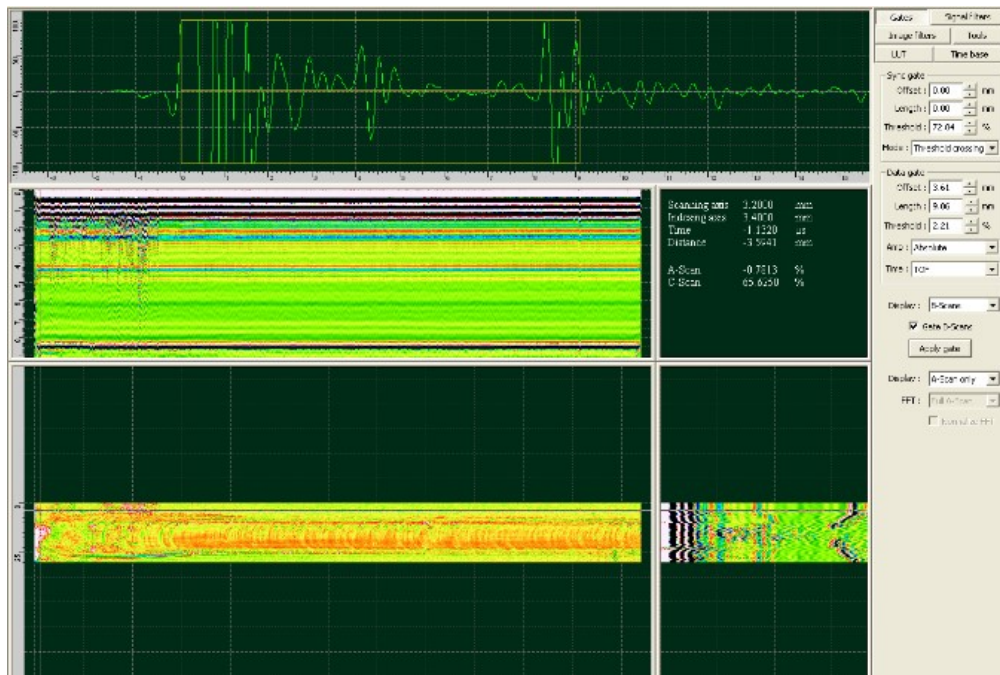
Test finaux 300 mm d'extrusion soudés (début de la zone soudée)
